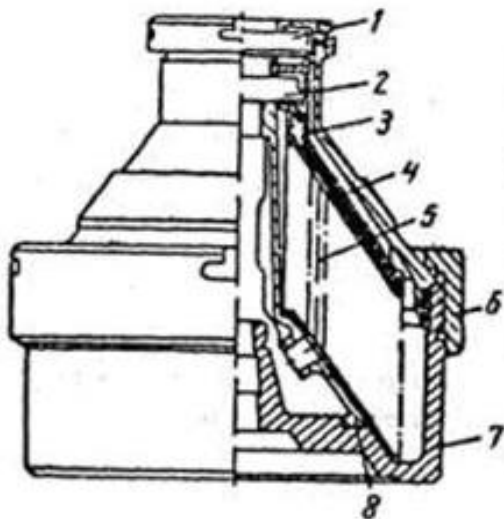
Барабан сепаратора: 1 – напірна камера знежиреного молока; 2 – напірна камера вершків; 3 – тарілка розділення; 4 – пакет тарілок; 5 – канал для молока в пакеті тарілок; 6 – велике затяжне кільце; 7 – основа барабана; 8 – тарілотримач
